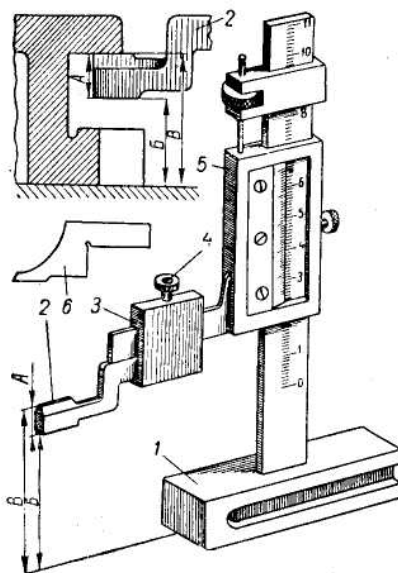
Конструкция штангенрейсмаса: 1 – основание; 2 – измерительная ножка; 3 – державка; 4 – стопорный винт; 5 – рамка, 6 – разметочная ножка
